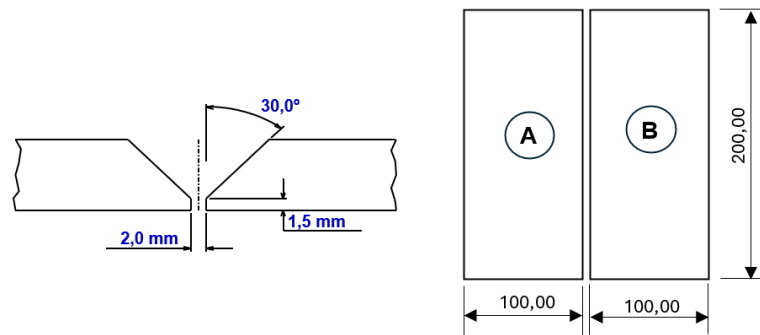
Croqui da chapa para Teste de Qualificação de Soldadores - Fonte: IT-ETM-001-23 – Instrução Técnica para Qualificação de procedimento de Soldagem, ETEMAN.
